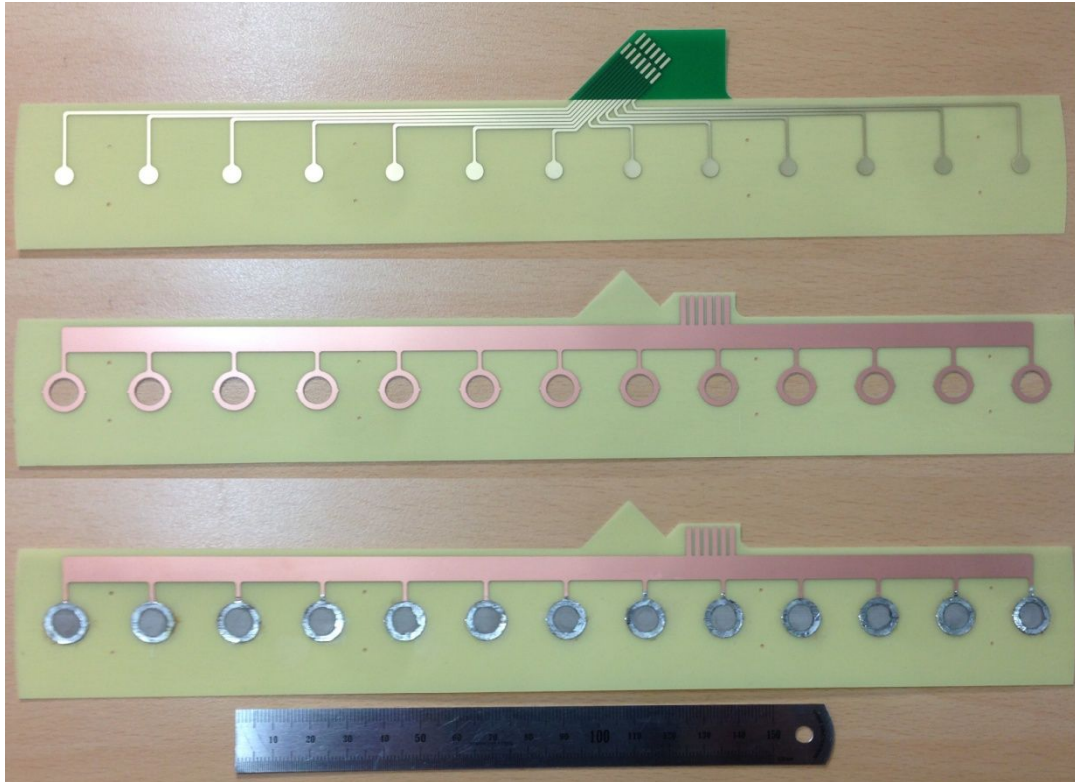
이온 에너지 분포 측정기 제작에 사용된 PCB.
